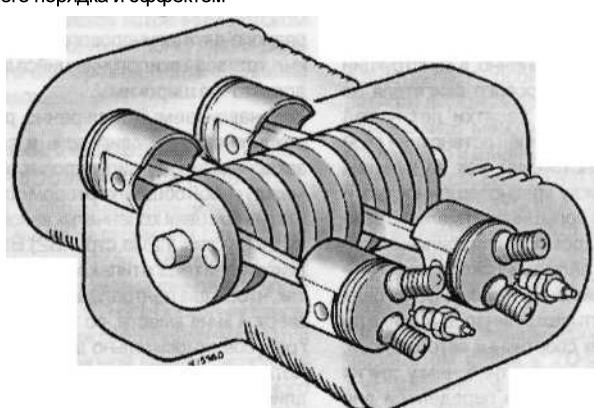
в Четырехцилиндровый оппозитный двигатель
